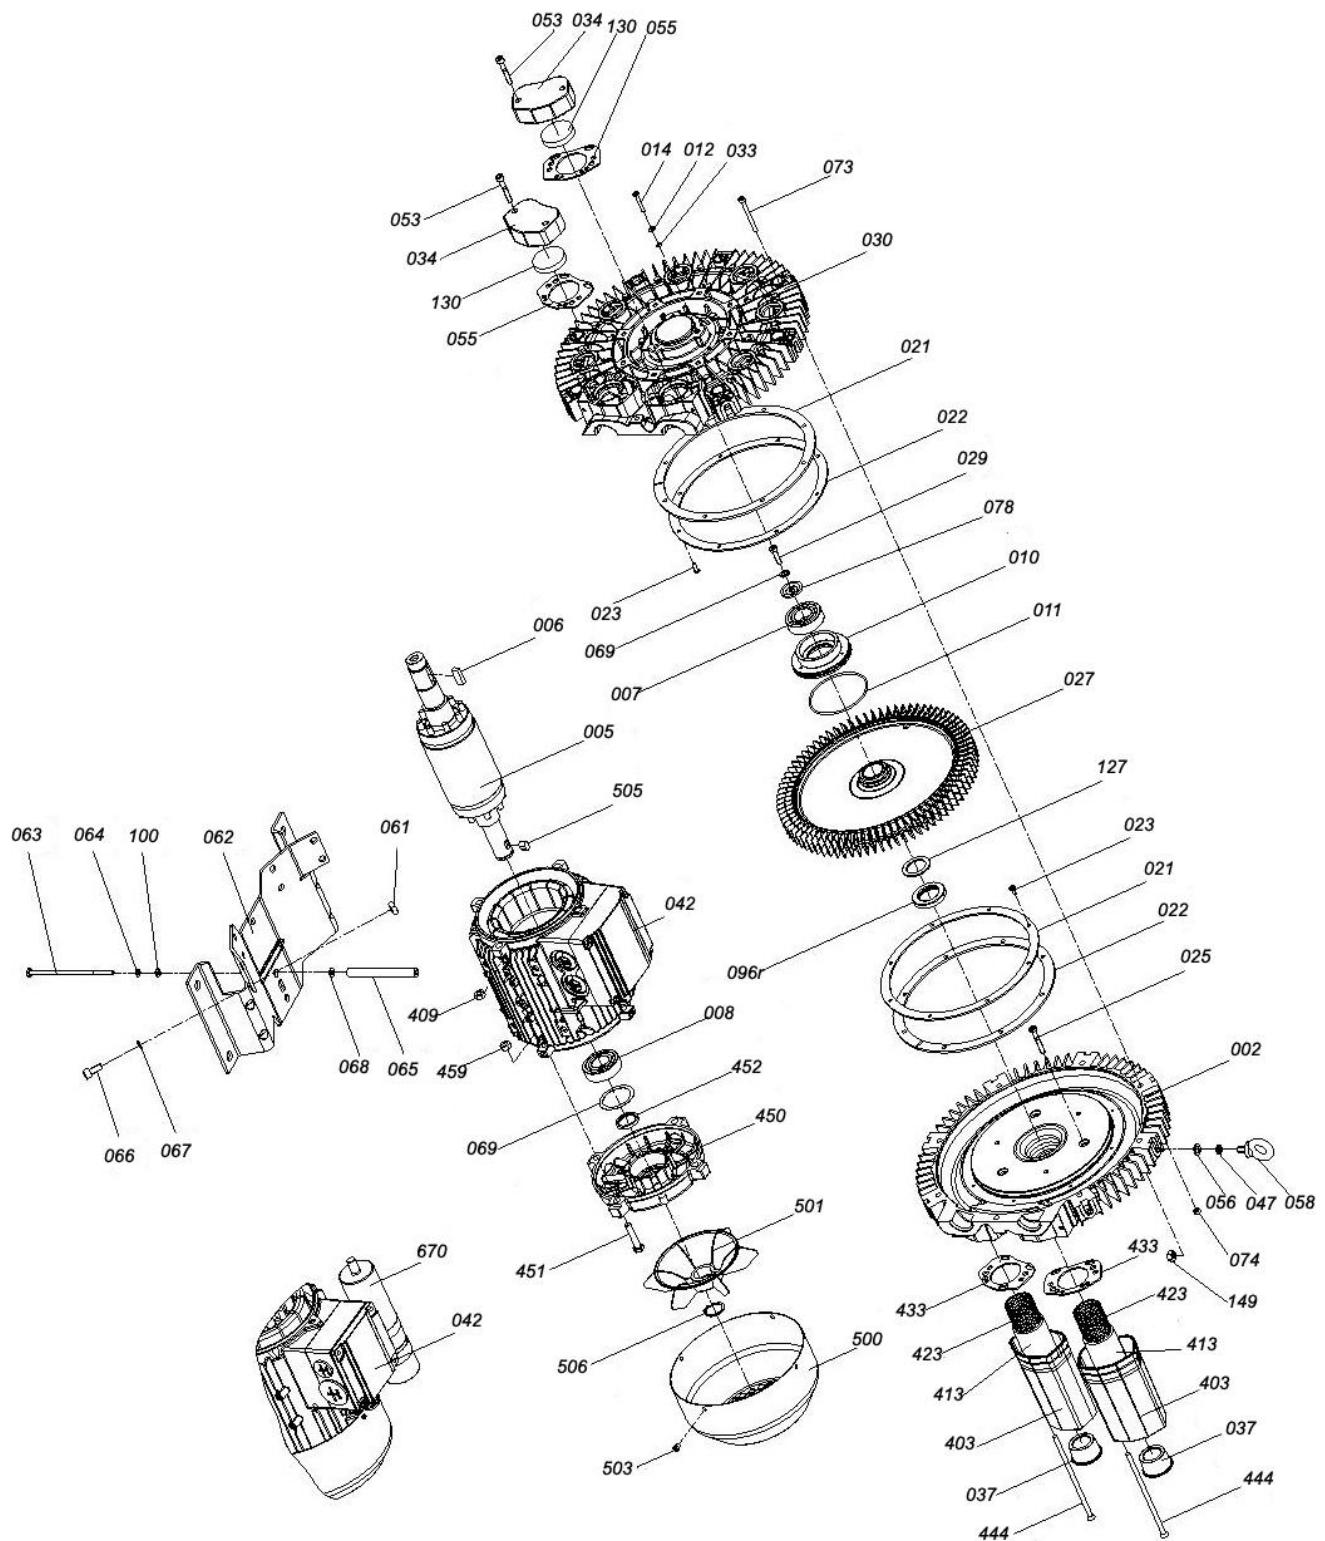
Деталировка одноступенчатых воздуходувок 4RB
